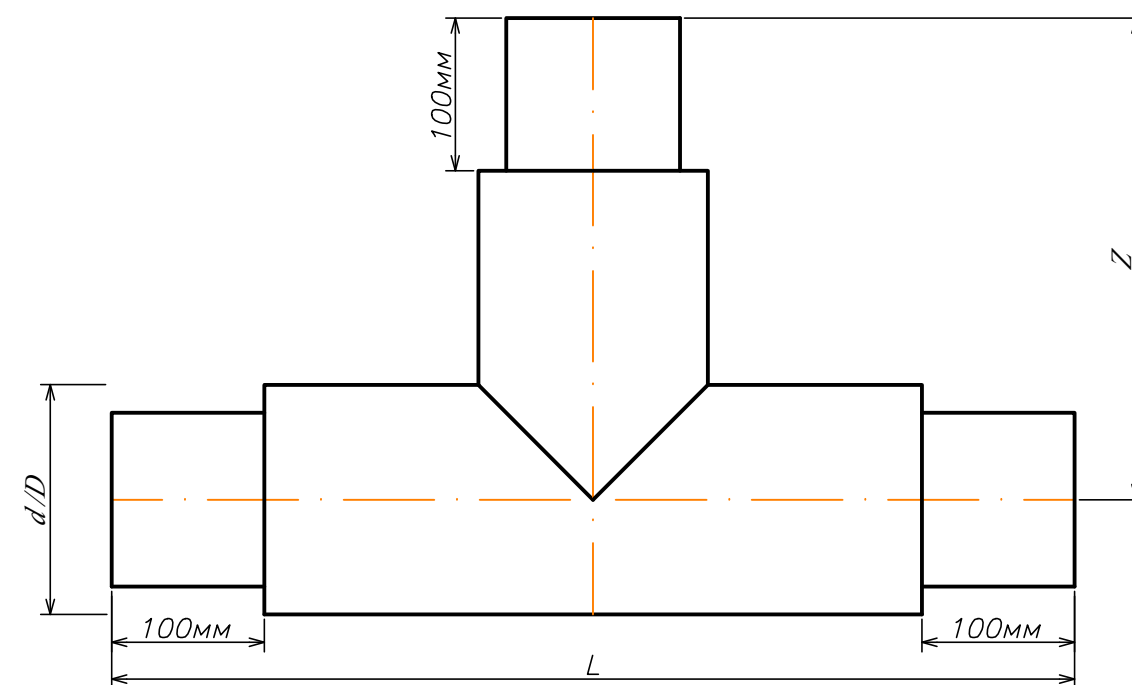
Тройник равнопроходной сварной предизолированный
